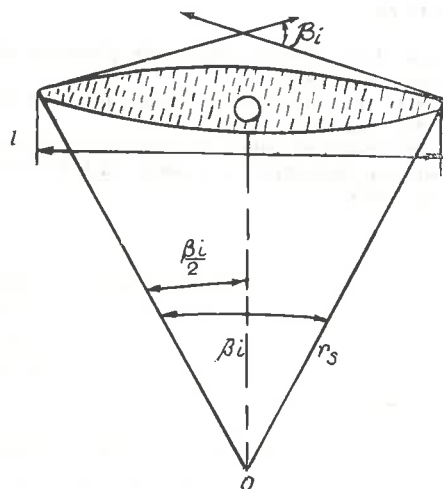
Schema constructivă pentru determinarea lungimii lamei sabotului de susţinere a cablului purtător.
